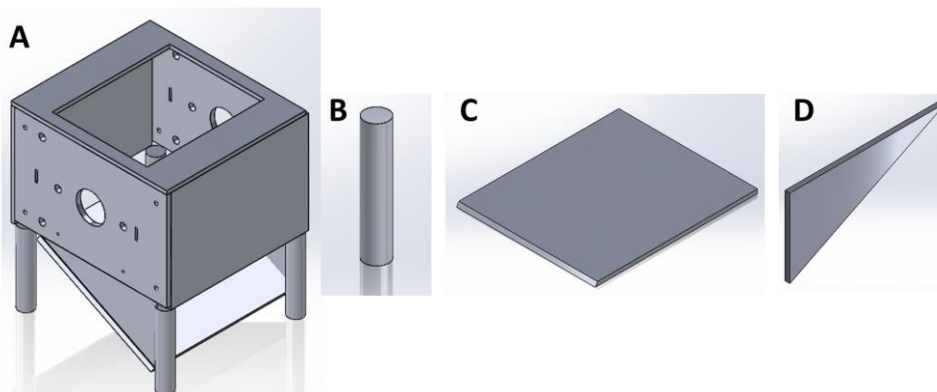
(A) Pré-montagem da base e seus componentes (B) chapa lateral, (C) chapa frontal e (D) tampa
